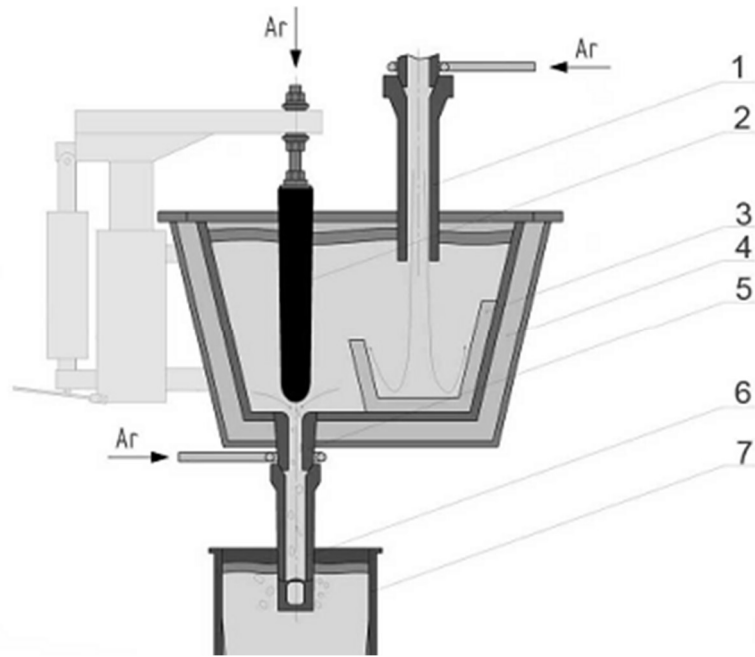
Схема движения стали из промковша в кристаллизатор: 1 – защитная труба; 2 – стопор; 3 – металлоприемник; 4 – промежуточный ковш; 5 – стакан-дозатор; 6 – погружной стакан; 7 – кристаллизатор.
